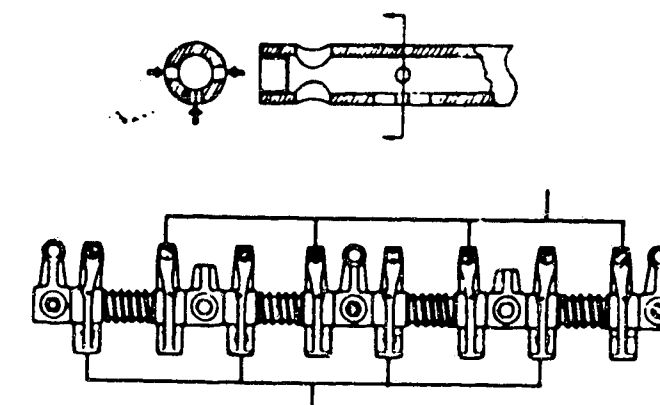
Motor 4A-C: Die Kipphebelwelle ist so einzubauen, dass die Ölbohrungen seitlich und gegen unten gerichtet sind.
